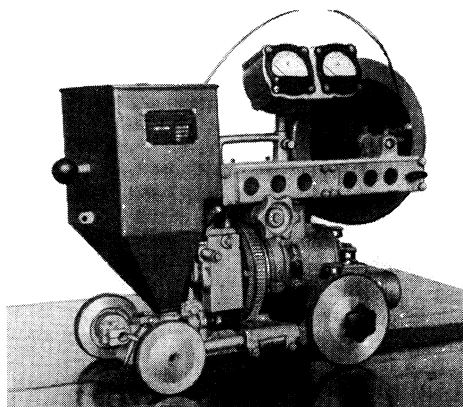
Сварочный трактор ТС-17МУ (АДФ-1002)
